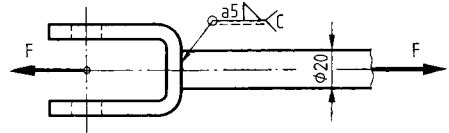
Geschweißter Zugstangenkopf
